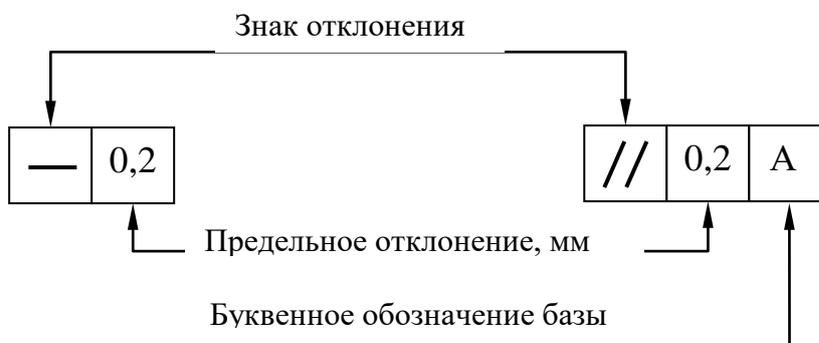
Структура обозначения допуска формы и расположения поверхностей
